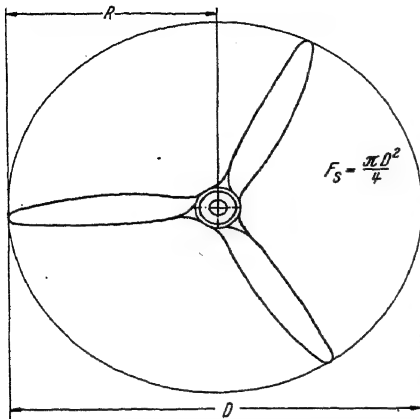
Erläuterung von Luftschraubendurchmesser R , Luftschraubendurchmesser D und Schraubenkreisfläche F_s .
